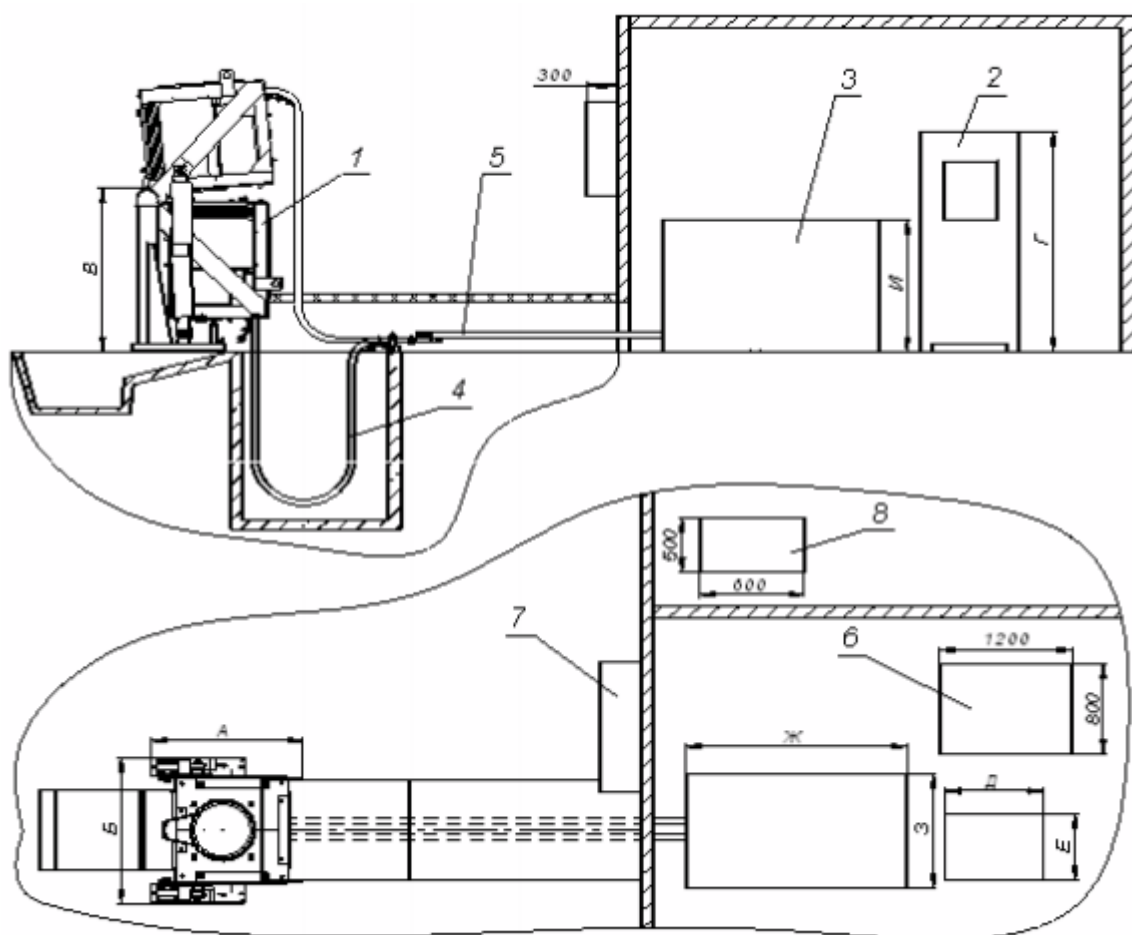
Загальний вигляд, габаритні розміри і розташування ІСТ-0,4:
